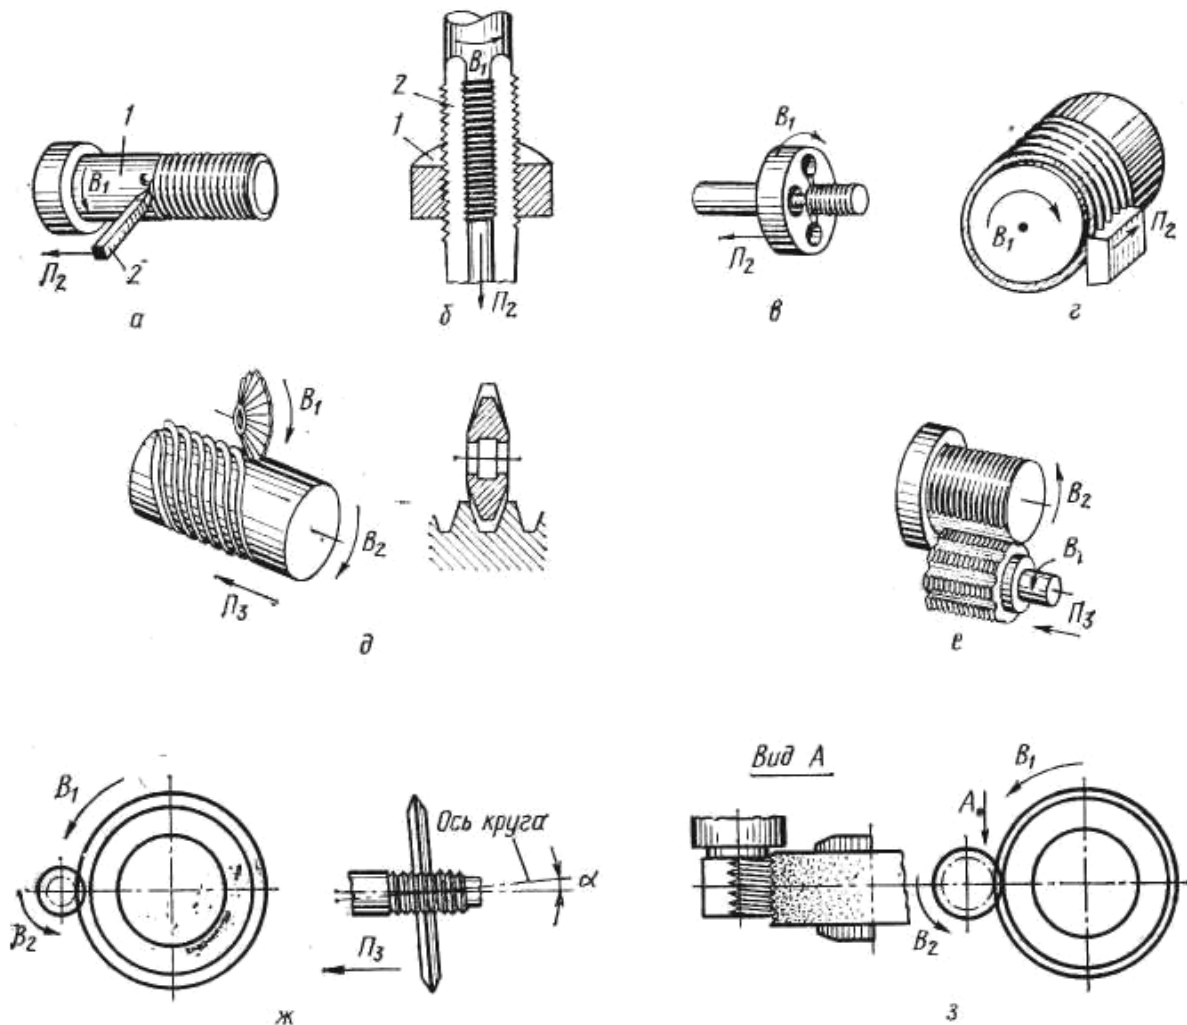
Формообразование винтовых поверхностей на заготовках различными режущими инструментами: *а* – резцовым резцом; *б* – метчиком; *в* – плашкой; *г* – резцовой гребенкой; *д* – дисковой резцовой фрезой; *е* – многониточной гребенчатой фрезой; *ж* – дисковым шлифовальным кругом; *з* – многониточным шлифовальным кругом
